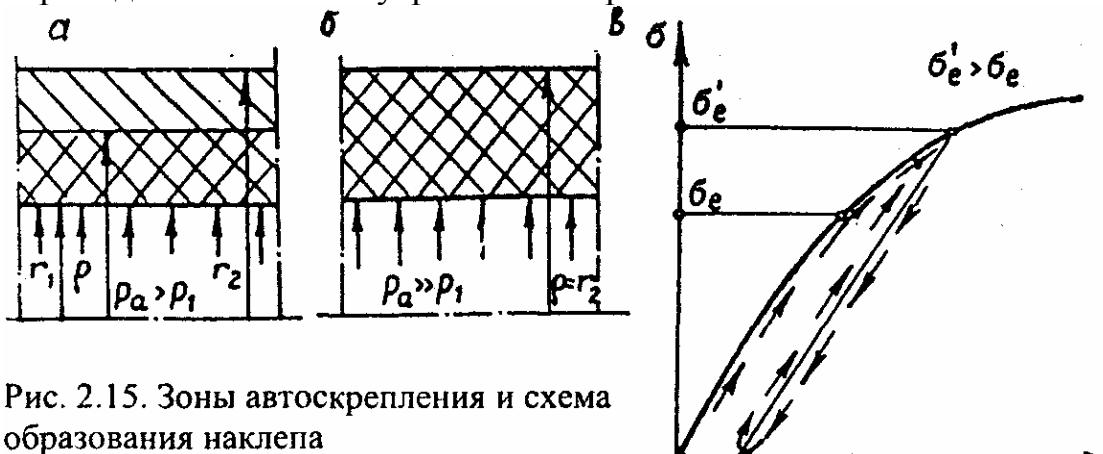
Зоны автоскрепления и схема образования наклена
